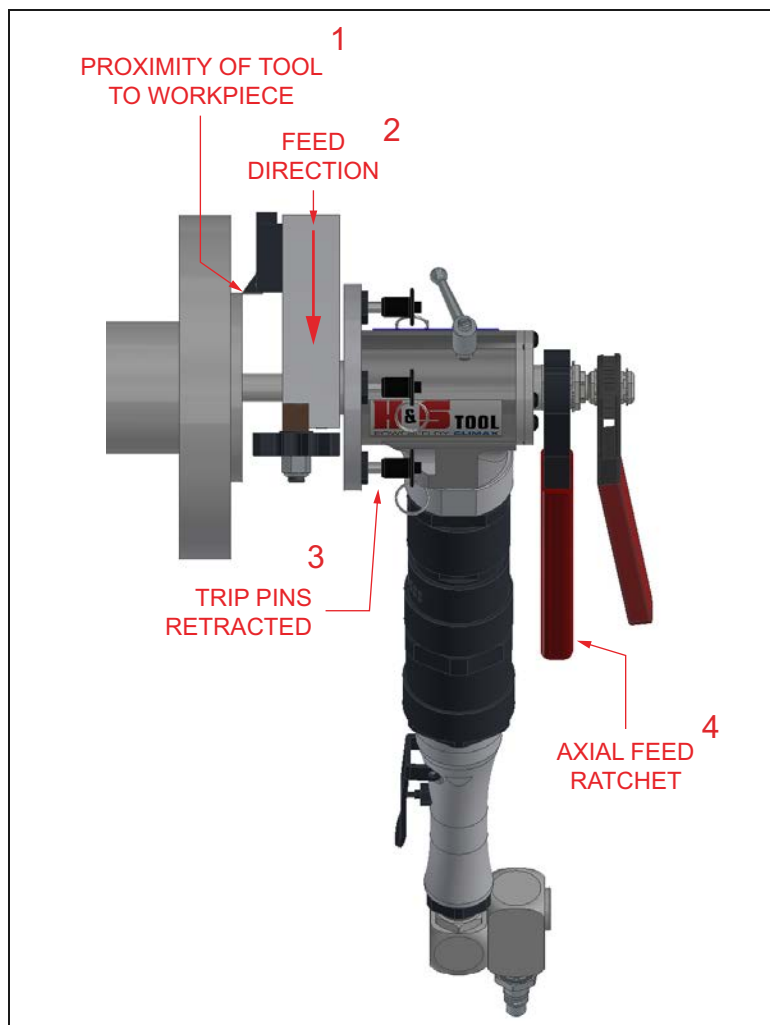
Осуществление осевой подачи и инструмент, касающийся обрабатываемой детали
